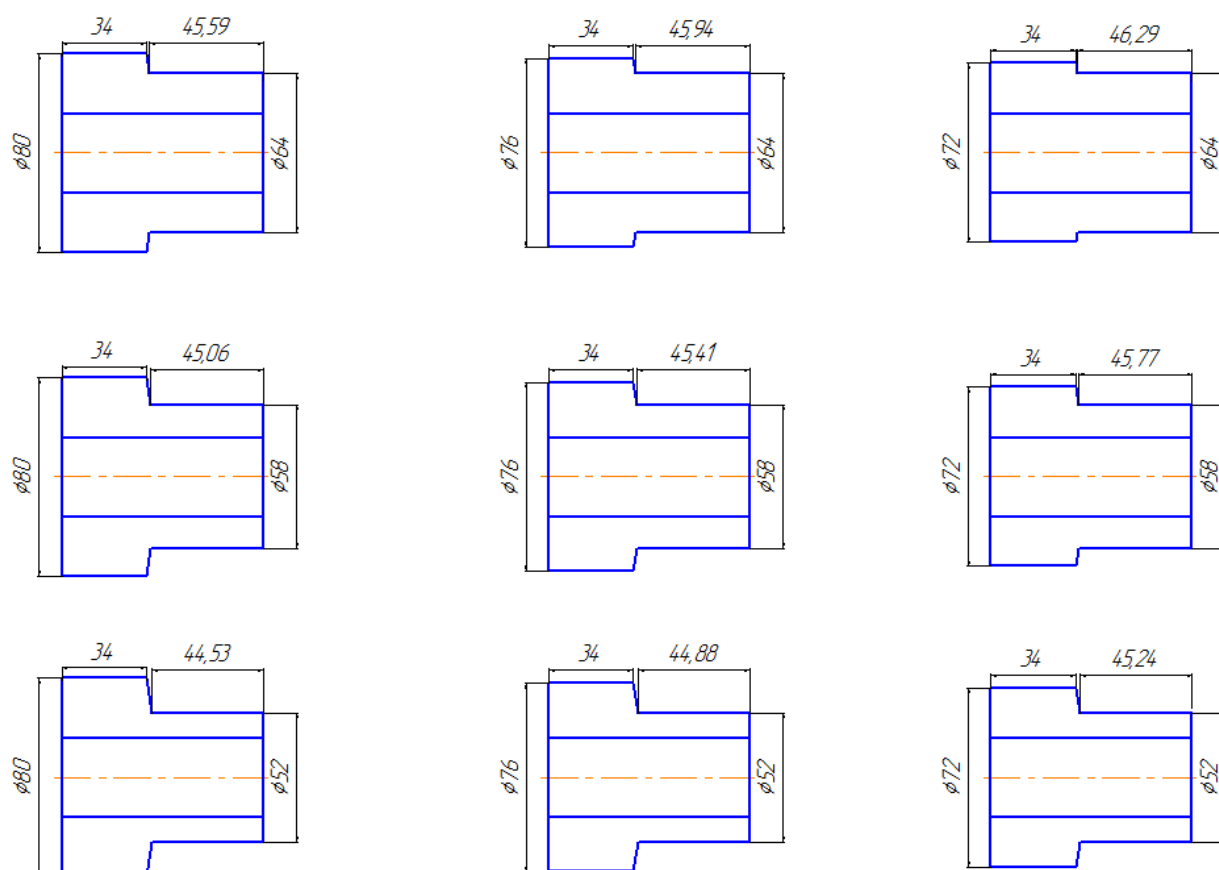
Форми та розміри досліджуваних заготовок
